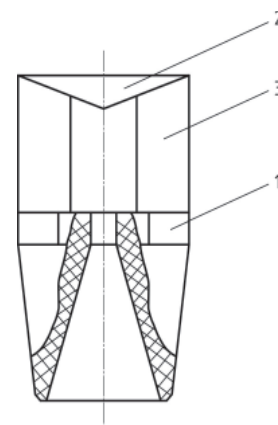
Дефлекторный ороситель кругового действия: 1 – корпус; 2 – конический дефлектор; 3 – ножка
